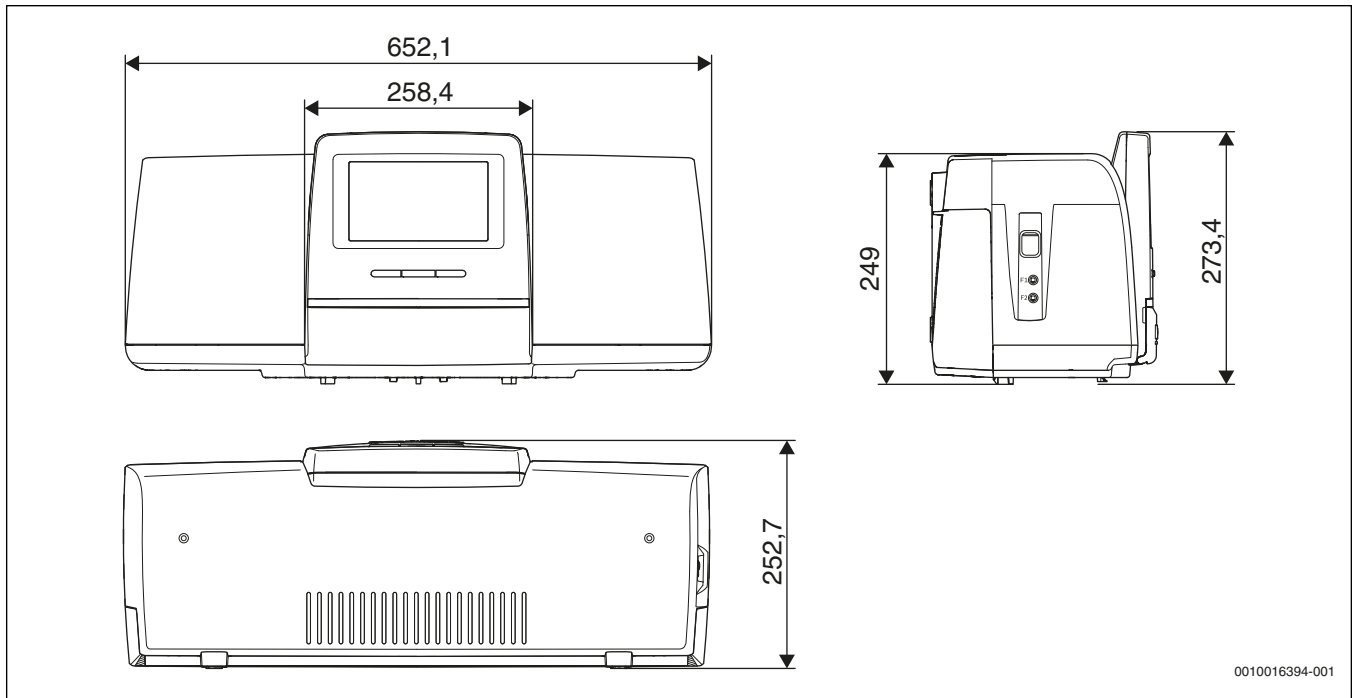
Dimensiones CC 8000 (medidas en mm)
